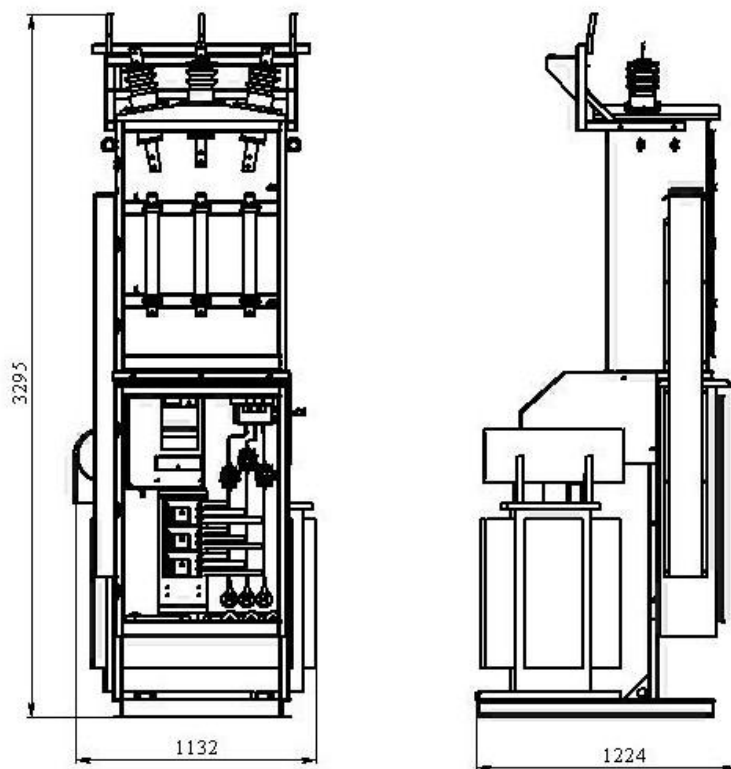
Габаритные и установочные размеры КТПН-Орб 07
